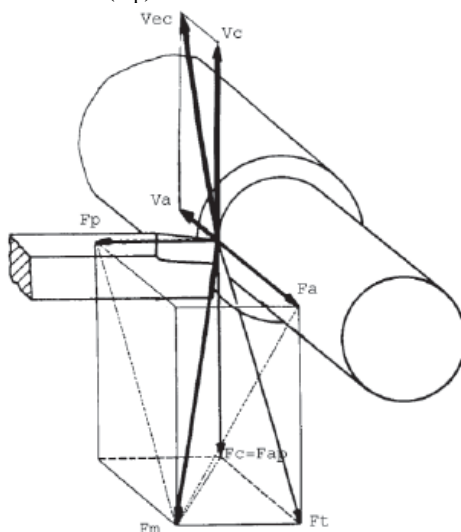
Componentes das forças de maquinagem no torneamento cilíndrico [32]
